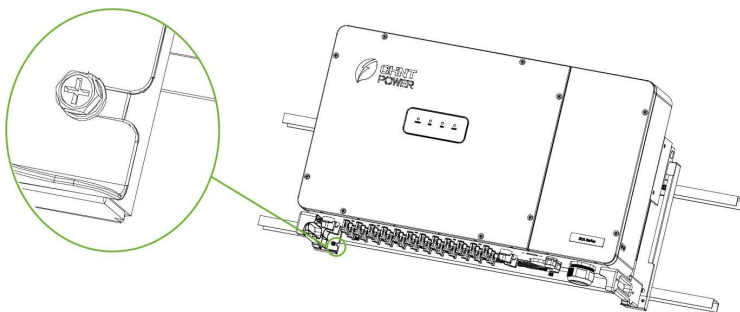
Inversor fixado no suporte do painel traseiro
